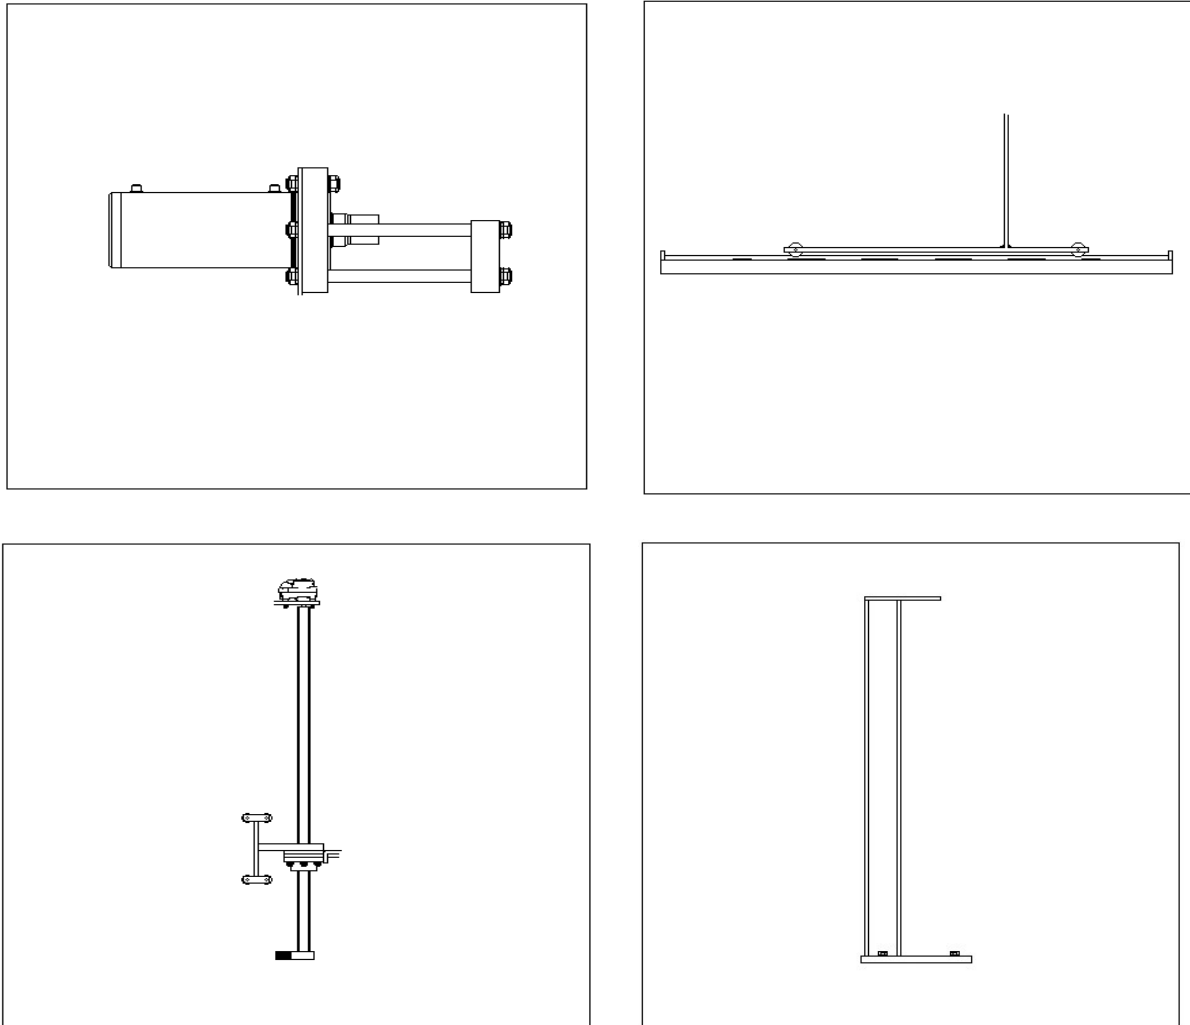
Els 4 conjunts que conformen la màquina, d'esquerra a dreta i de dalt a baix: conjunt extractor; conjunt de desplaçament transversal, conjunt de desplaçament vertical, conjunt estructural
